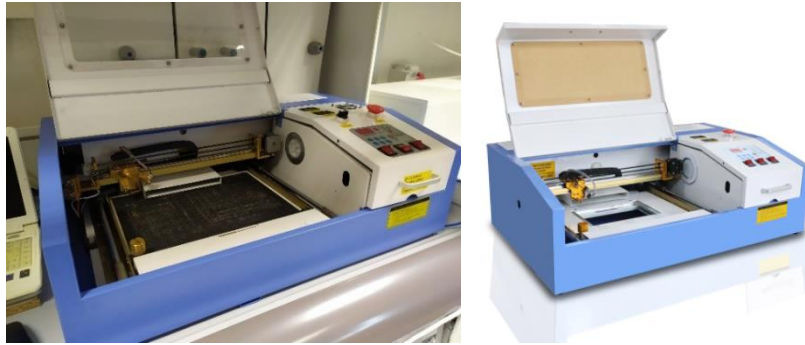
Equipo de corte por láser de CO₂ Liaocheng City Hengchunyuan Machinery Equipment Co., Ltd FL-K40. [Fuente.](#)
